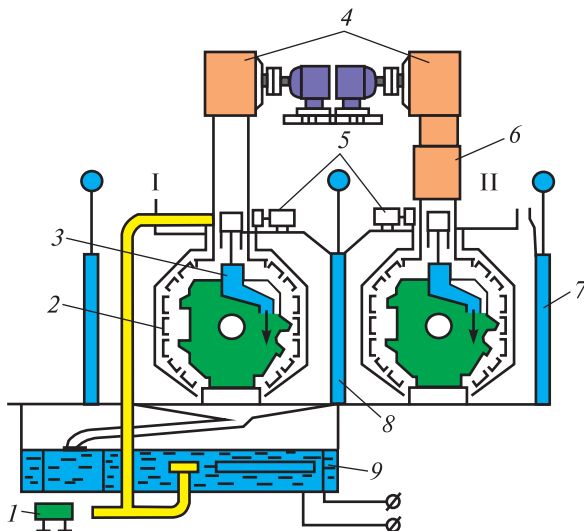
Двухкамерная машина для наружной обмывки и сушки тяговых двигателей перед разборкой
